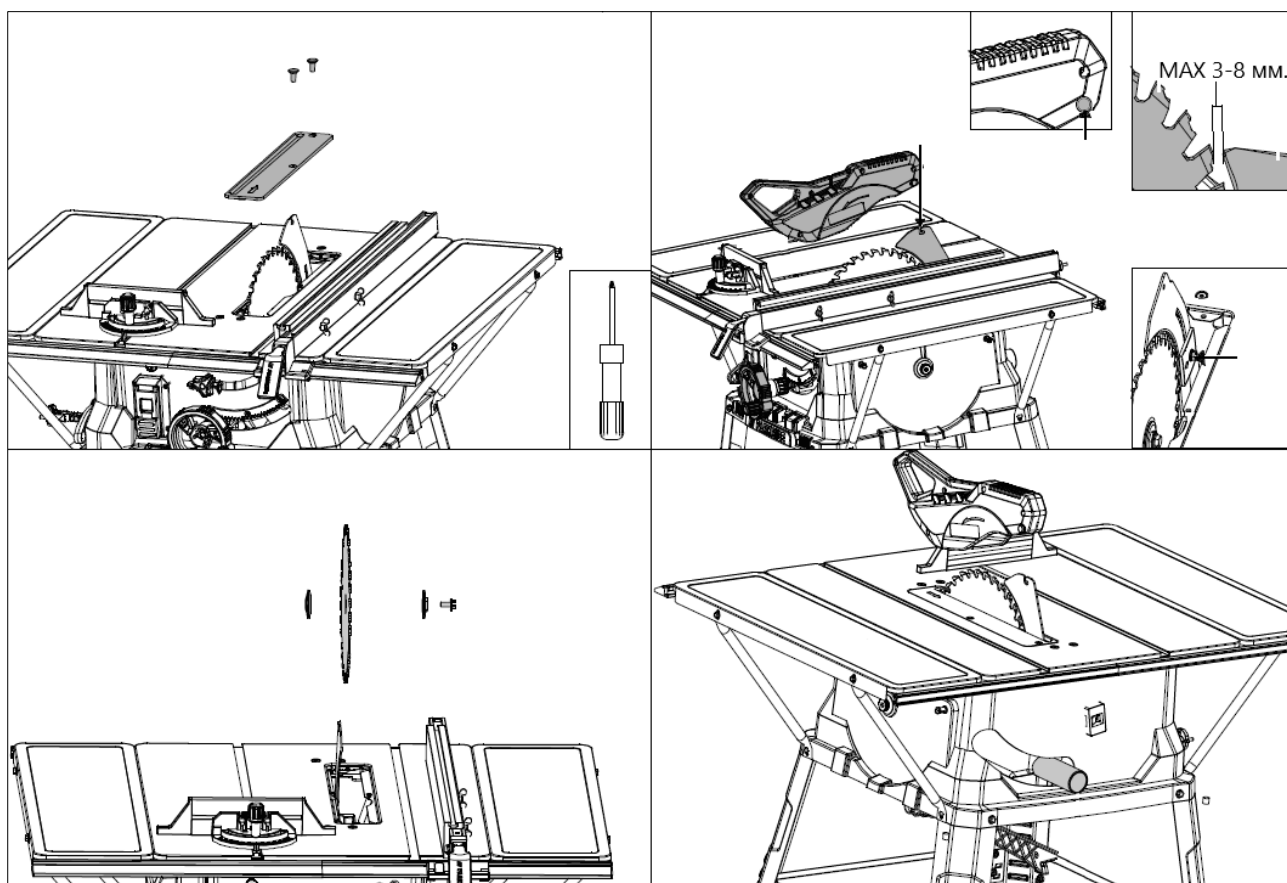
Регулировка расклинивающей пластины, установка защитного кожуха, замена диска.
